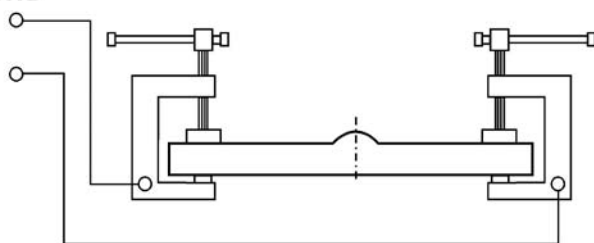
Схема подключения образца к установке при проведении ЭФО металла сварных соединений
